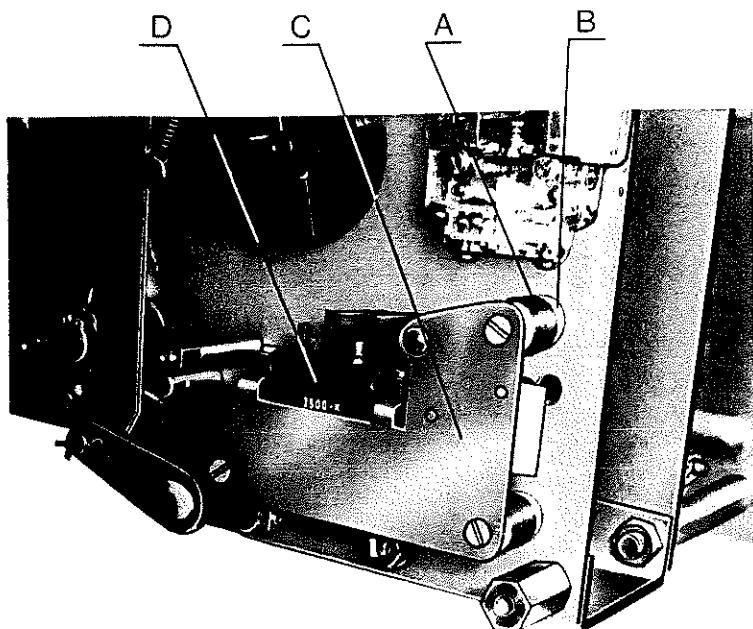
Montaggio del dispositivo di protezione del motore caricamolle
